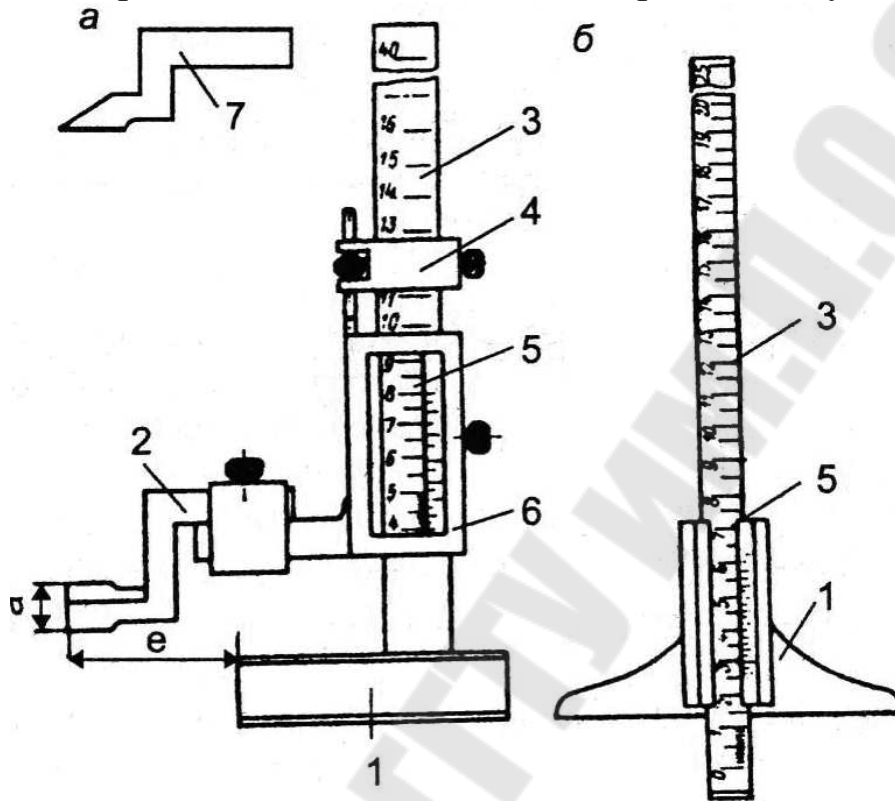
Штангенрейсмас (а) и штангенглубиномер (б): 1 основание; 2- измерительная ножка; 3 – штанга; 4- рамка с микрометрической подачей; 5- нониус; 6 – рамка; 7 –разметочная ножка.
